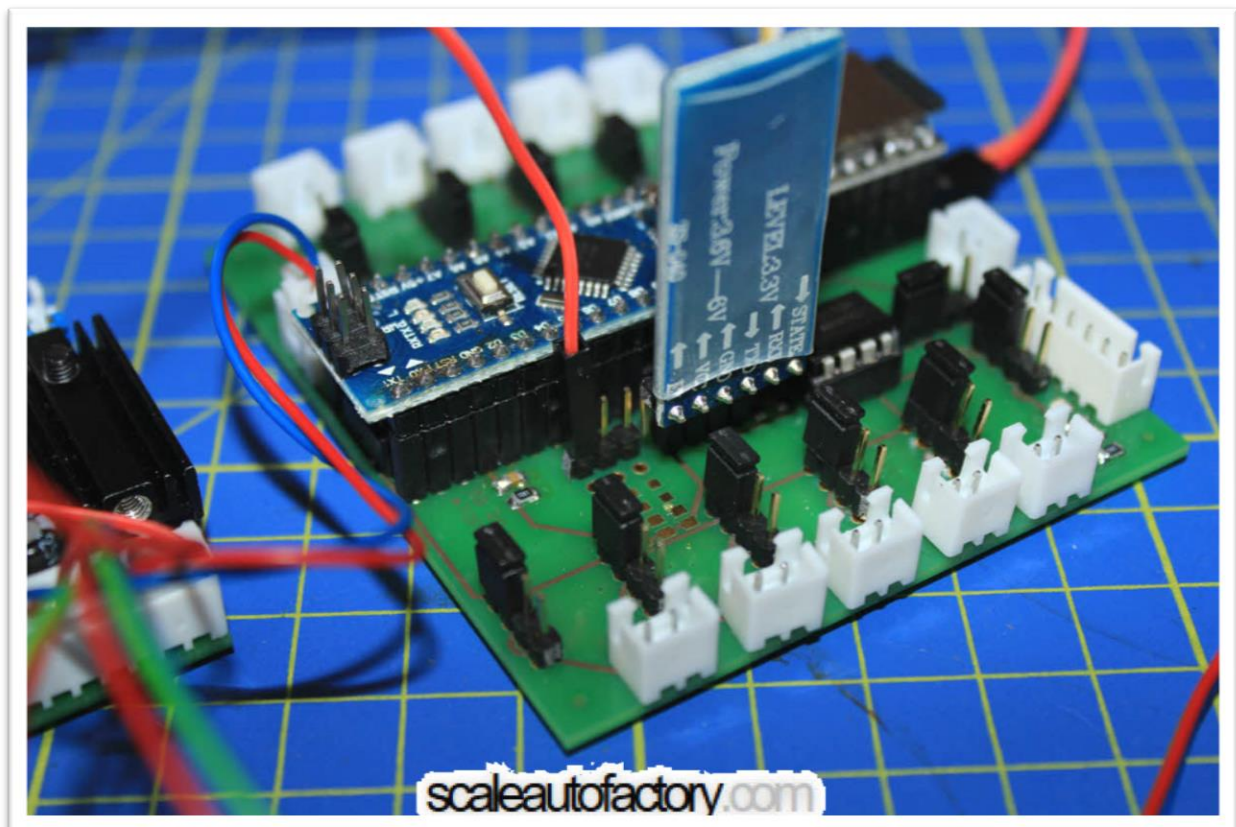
Support Board Farbwechsel-Steuerkabel Anschluss
